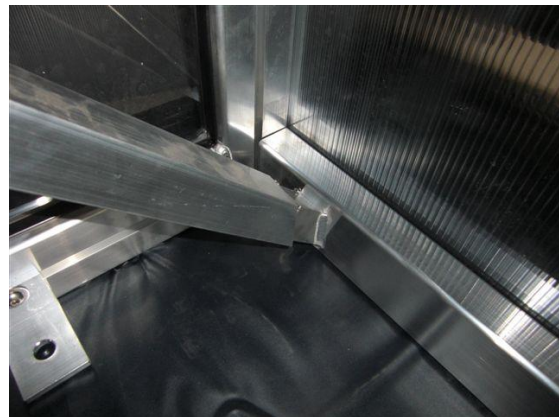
Mittelunterstützungen auf die schräg an die Rückwand angeschweißten Zapfen stecken. Beachten, dass die beiden Mittelunterstützungen mit den 5 Stück Einsteckmutter auf die äußeren Zapfen gesteckt werden. Die jeweils hintere Einsteckmutter M8x20 über dem 9mm-Loch positionieren und von unten mit Sechskantschraube M8x45 verschrauben.
